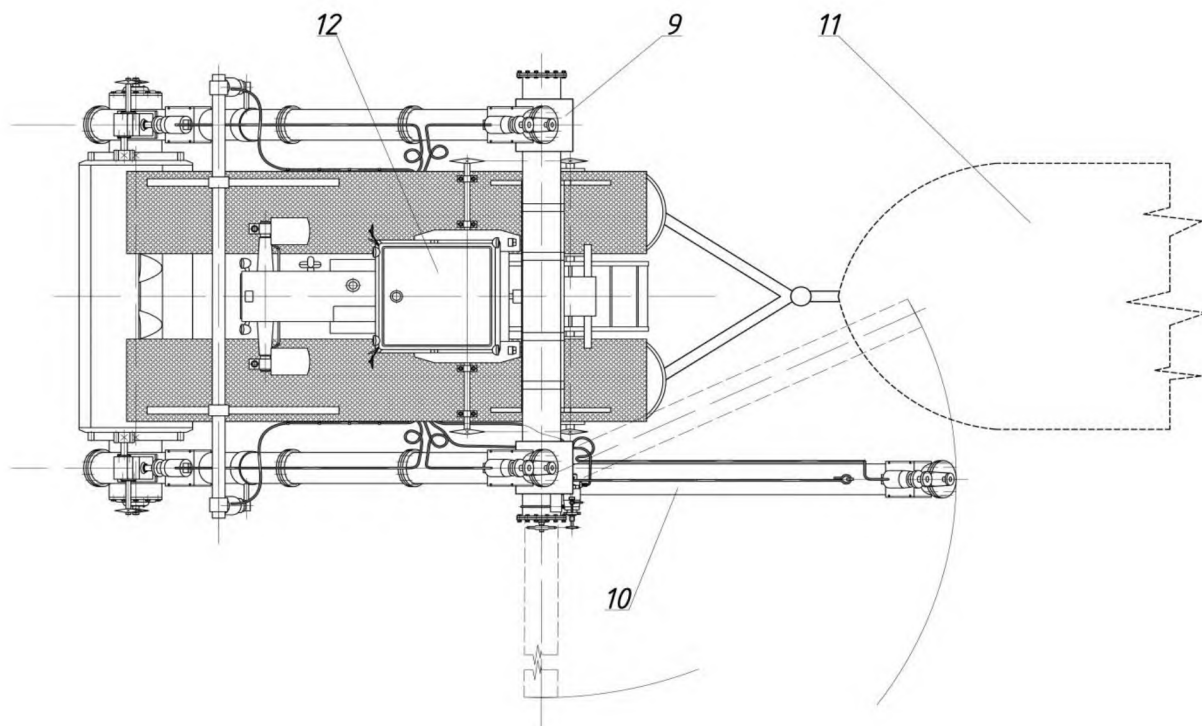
Конструктивна компоувальна схема сапропеледобувного модуля для добування органічної сировини(вид зверху): 1 – добувна фреза; 2 – нерухомий корпус; 3 – центральний шнек; 4 – гвинтовий прес; 5 – з’єднувальний рукав; 6 – гідродвигун; 7 – редуктор; 8 – гідроциліндр; 9 – приймальний бункер; 10 – вивантажувальний шнек; 11 – ємкість готової сировини(баржа); 12 – трактор класу тяги 1,4; 13 – понтон; 14 – патрубок скидання вільної води; 15 – рульове кермо; 16 – лопатеве колесо;
